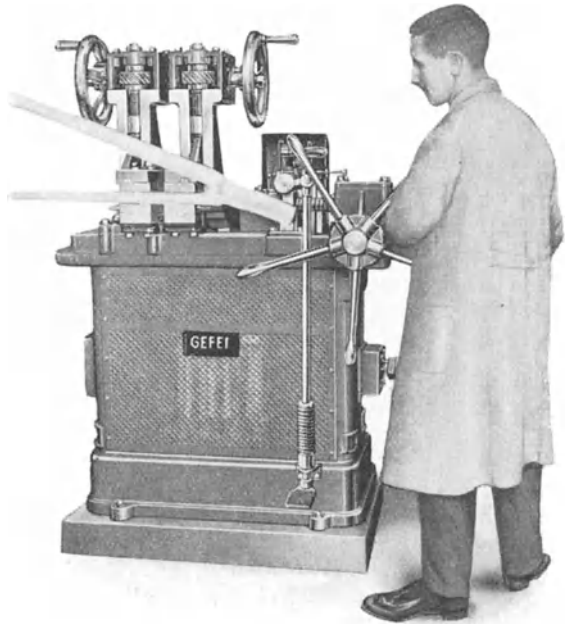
Mittelgroße Stumpfschweißmaschine.
